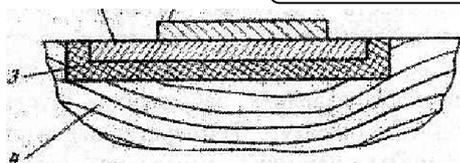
Прямка металлических листов: 1 - обрабатываемая деталь; 2 - массивная металлическая пластина; 3 - битумизированный войлок; 4 - стол.
